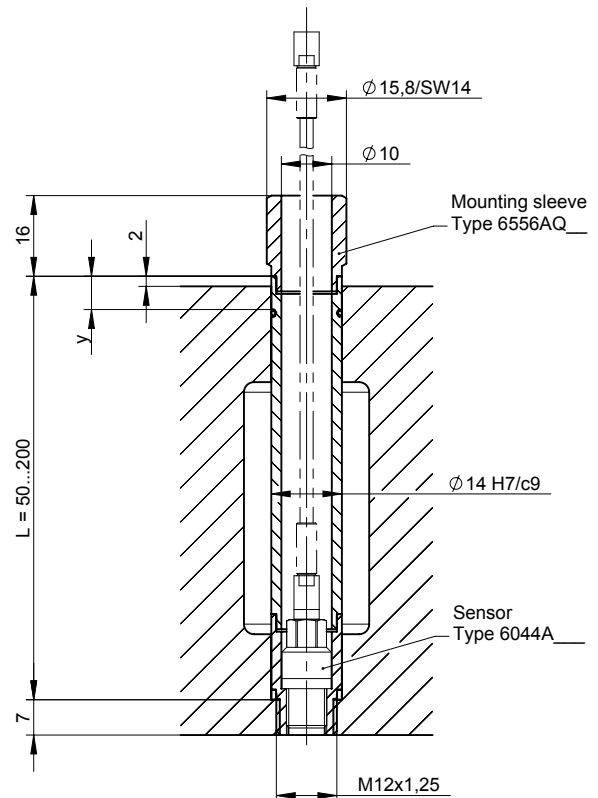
Einbau mit Montagehülse Typ 6556AQ...
